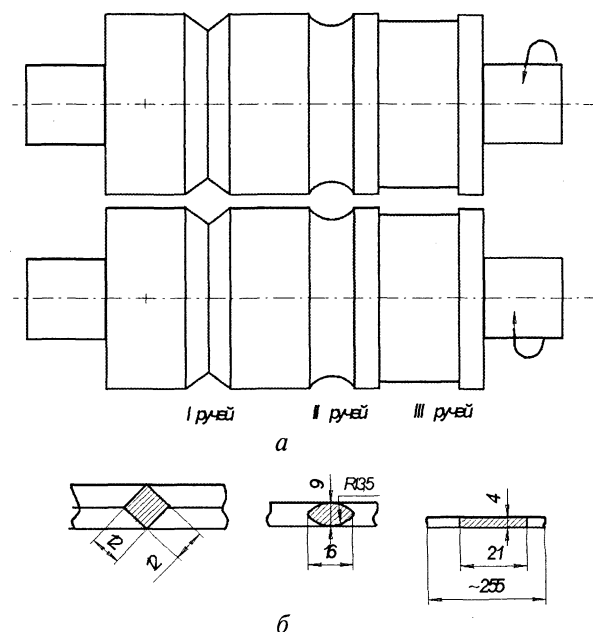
Схема прокатки: а – калибрующие валки; б – профили заготовки, получаемые в соответствующих ручьях валков
